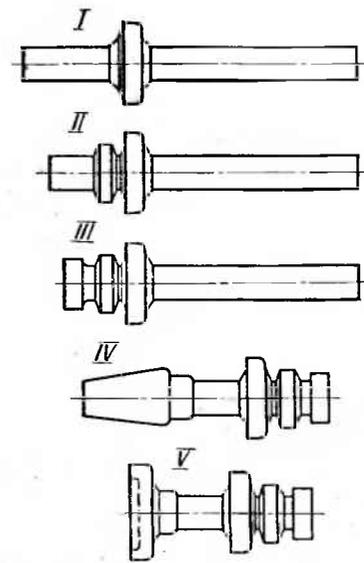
Переходы (I—V) высадки поковки блока зубчатых колес (шестерен)
